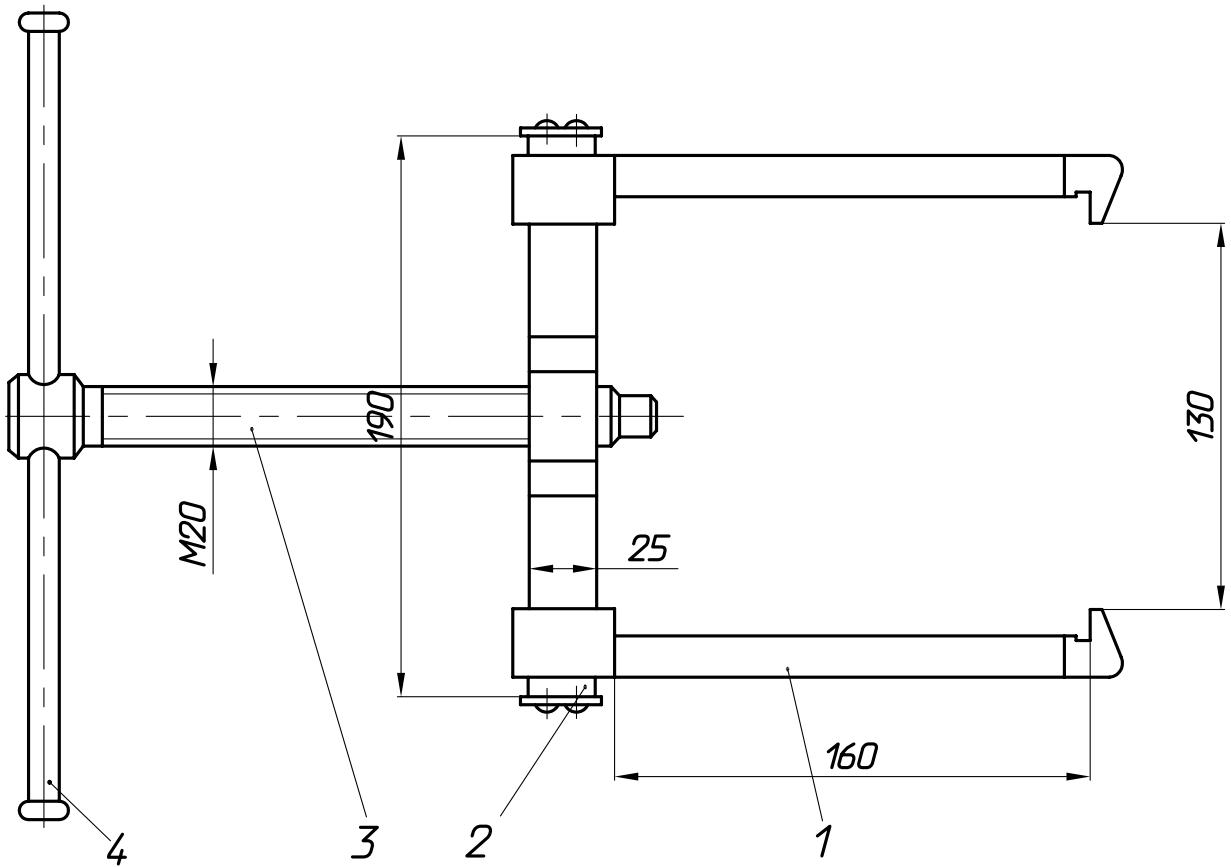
Съемник противовеса и шестерни коленчатого вала
